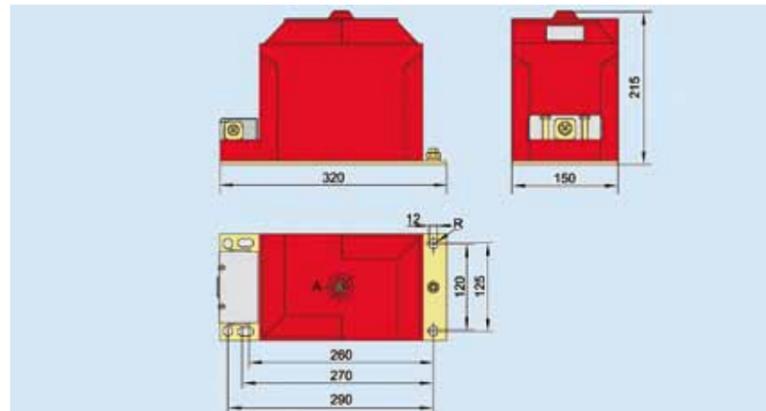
Внешний вид и монтажные размеры трансформатора напряжения JDZX10-6
